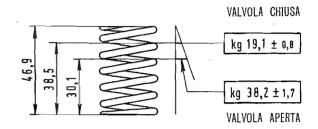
Dati principali, per il controllo della molla esterna per valvole, del motore 110 F.000.
